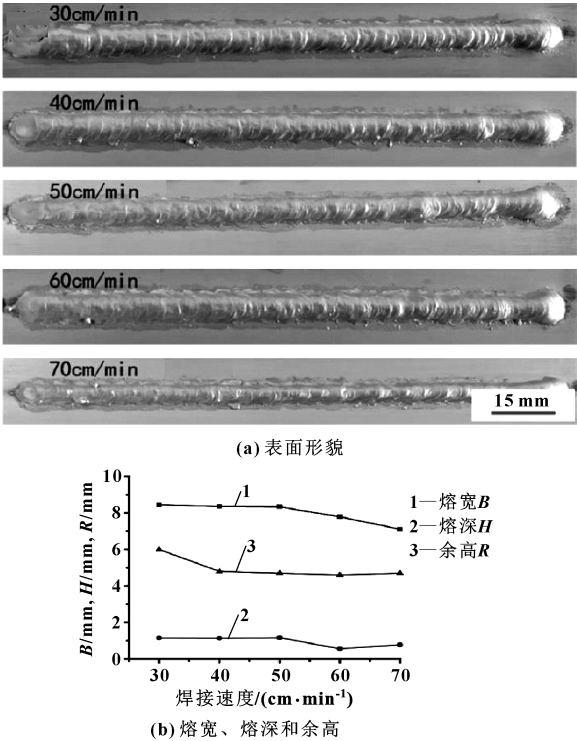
不同焊接速度下焊缝的表面形貌以及熔宽、熔深和余高
